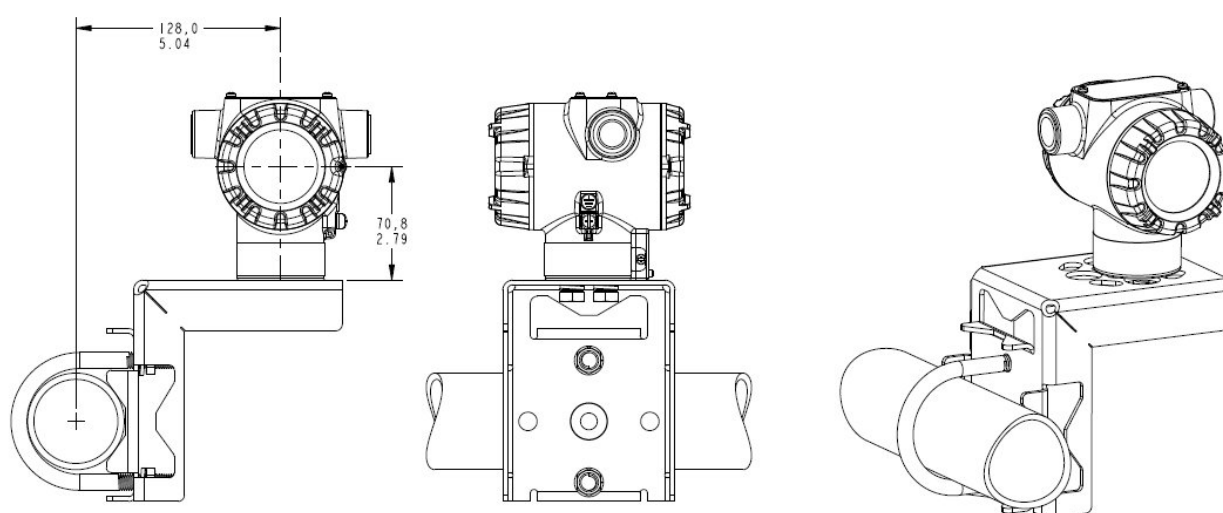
STT750 Монтаж на горизонтальную трубу при помощи угловой монтажной скобы
